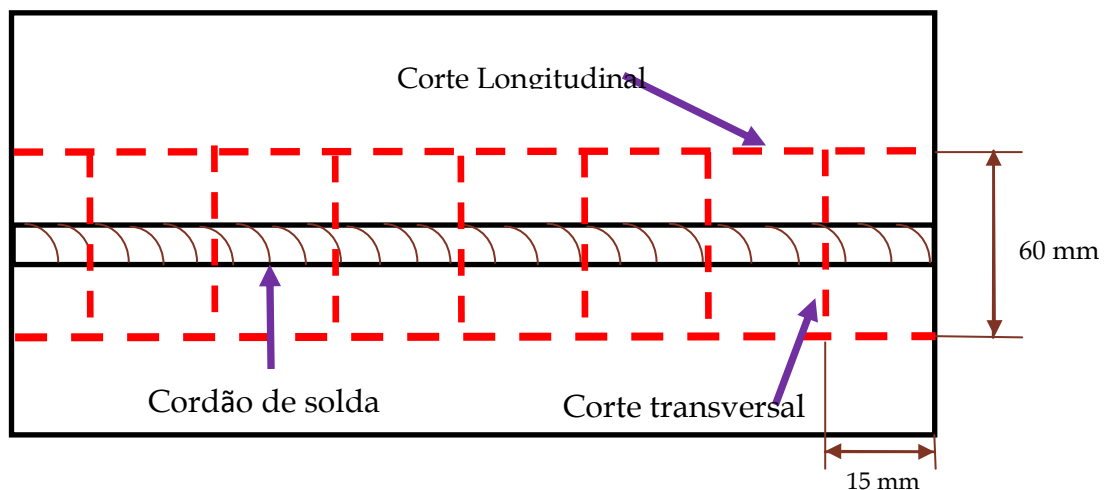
Execução do corte na chapa soldada do AISI 304L.
